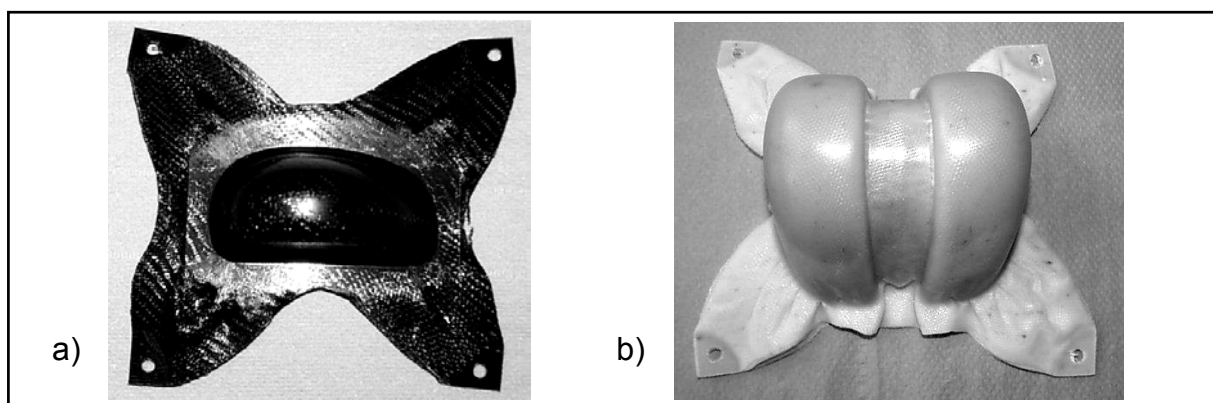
Umgeformte Prototypen mittels a) Einzel-, b) Doppelwerkzeug
